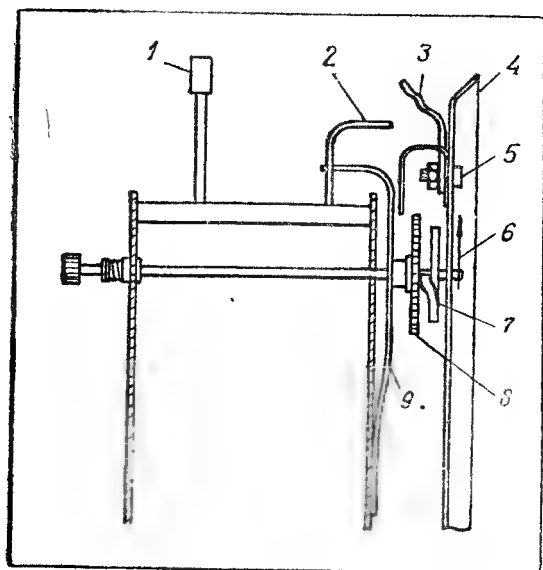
Положение рычага 9 и шестерни 8 до начала действия звонка будильника
